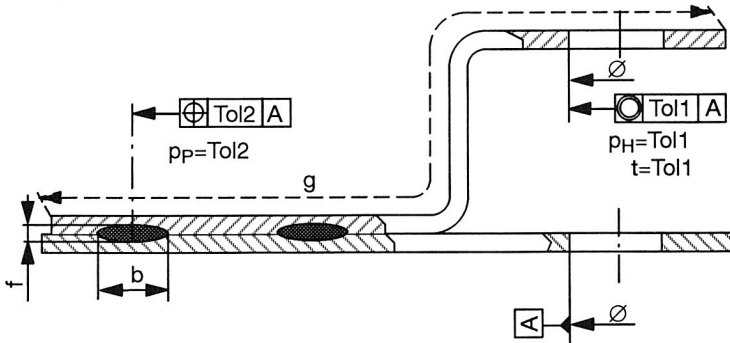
Die charakteristischen Geometrie Größen für eine Punktschweißverbindung
